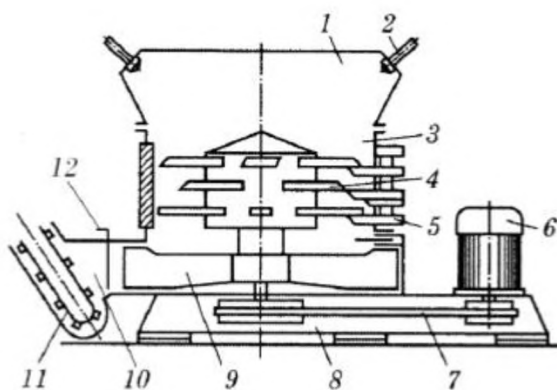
Подрібнювач-змішувач ИСК-3А . 1 – приймальна камера; 2 – форсунка розпилювач; 3 – робоча камера; 4 – ротор з ножами; 5 – нерухомі ножі; 6 – електропривод; 7 – клинопасова передача; 8 – рама; 9 – лопать; 10 – розвантажувальна камера; 11 – розвантажувальний транспортер
